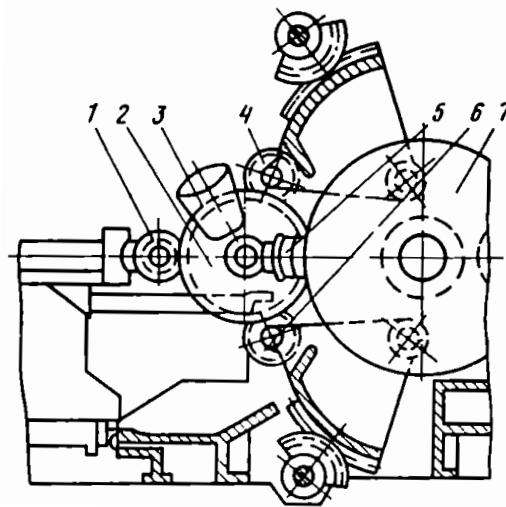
Схема прокатки на колесопрокатном стане вертикального типа: 1, 4, 6 – направляющие ролики, 2 – заготовка колеса, 3 – боковые валки, 5 – эджерные валки, 7 – нажимной валок [3]
